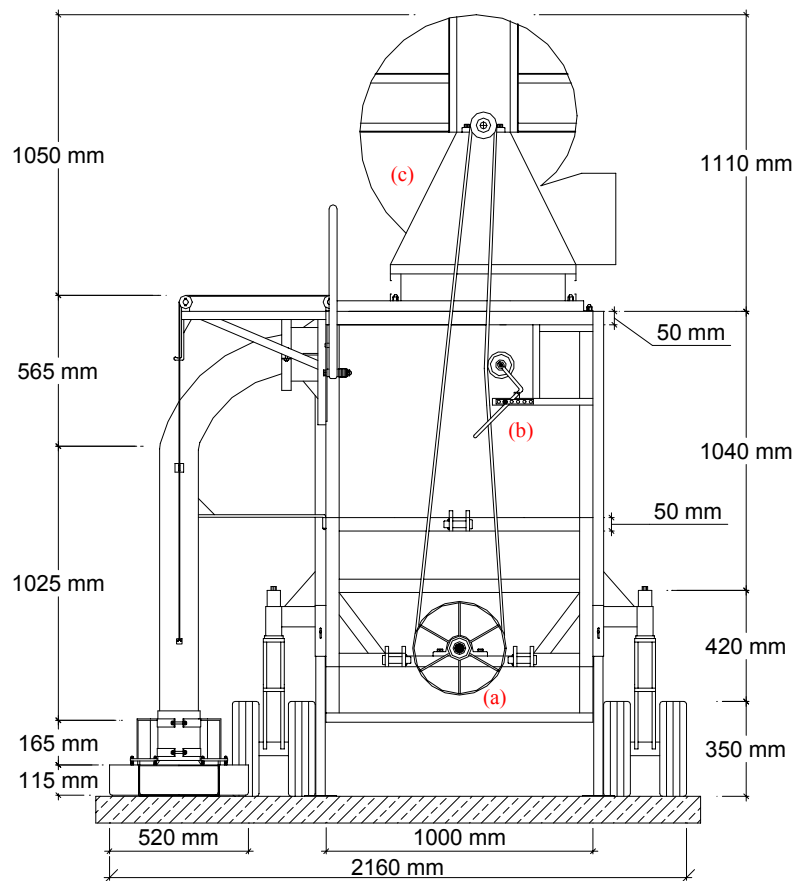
Vista frontal da máquina recolhadora de frutos de café. Componentes: (a) polia fixada à estrutura da máquina; (b) esticador de correia; e (c) ventilador centrífugo.
